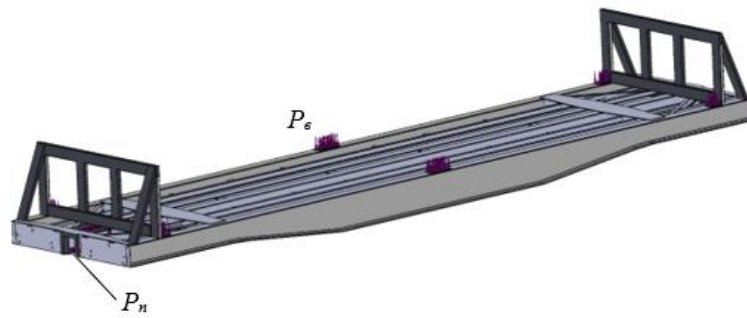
Розрахункова схема несучої конструкції вагона-платформи
